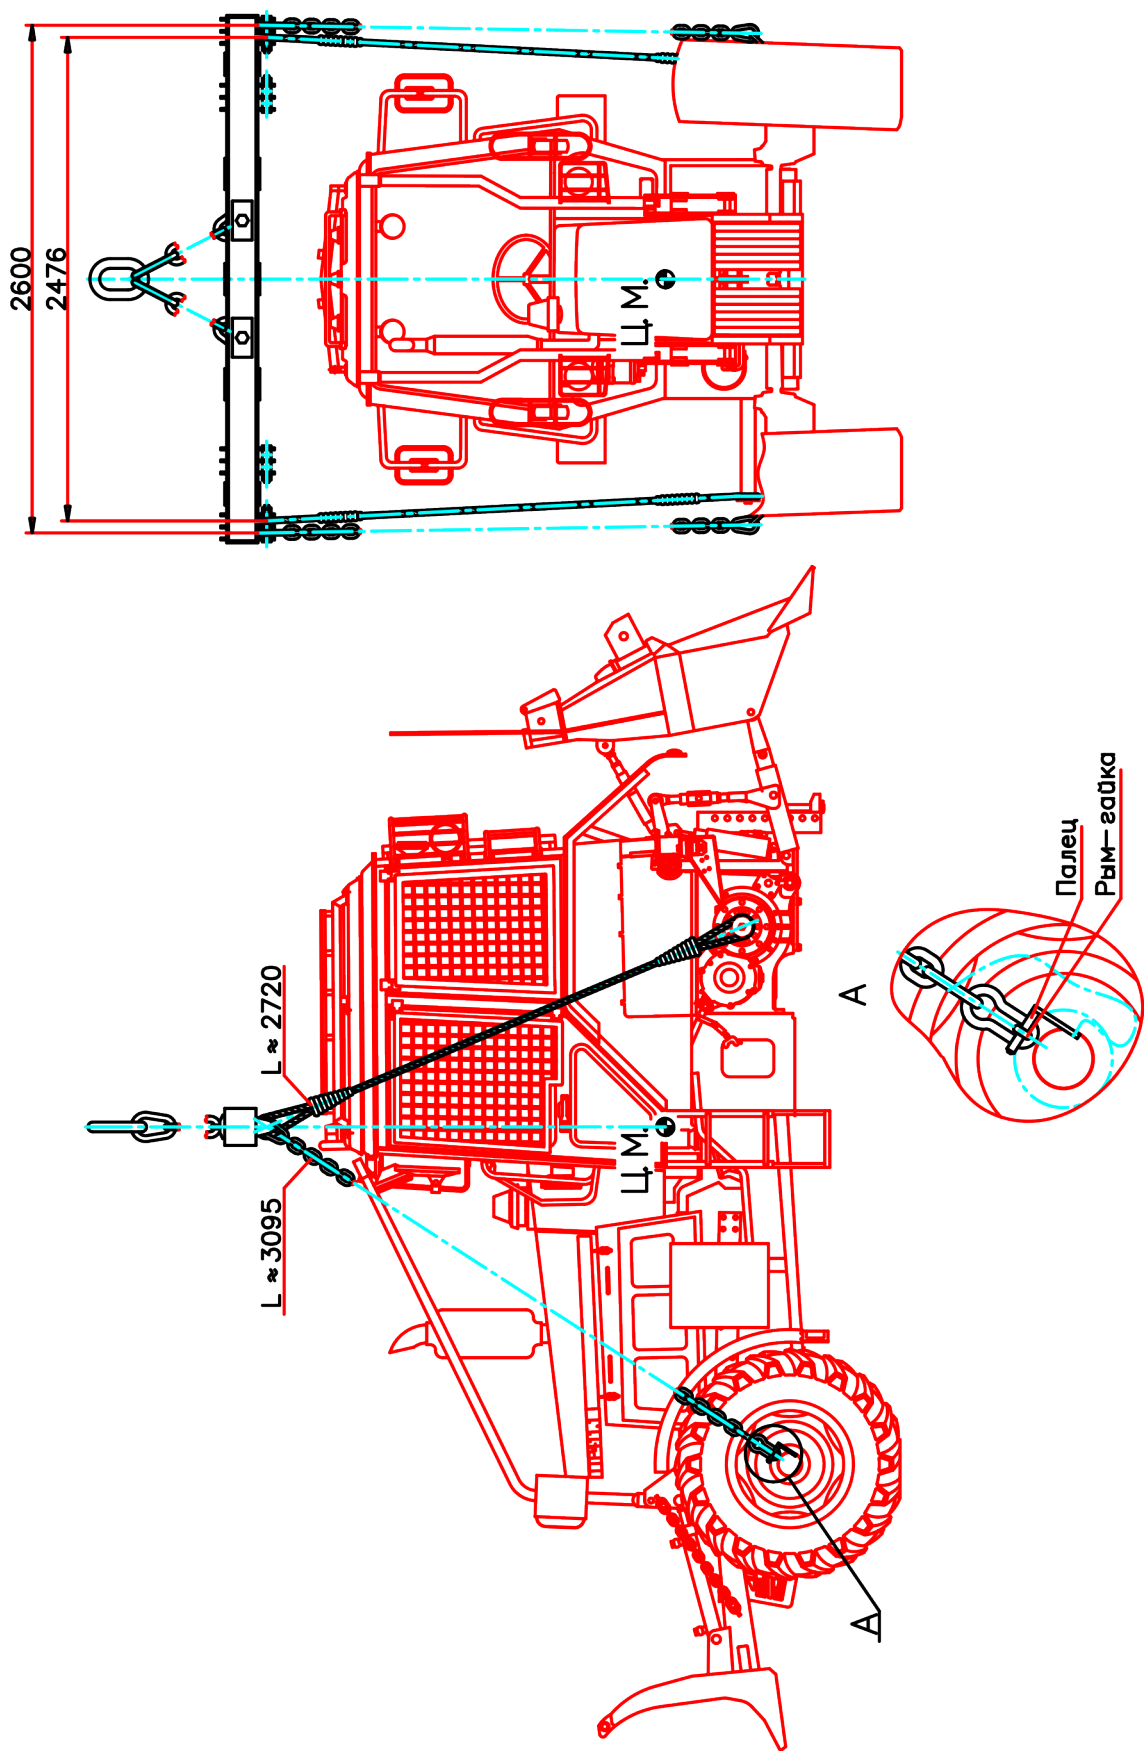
Схема строповки трелевочного трактора со снятыми задними колесами
